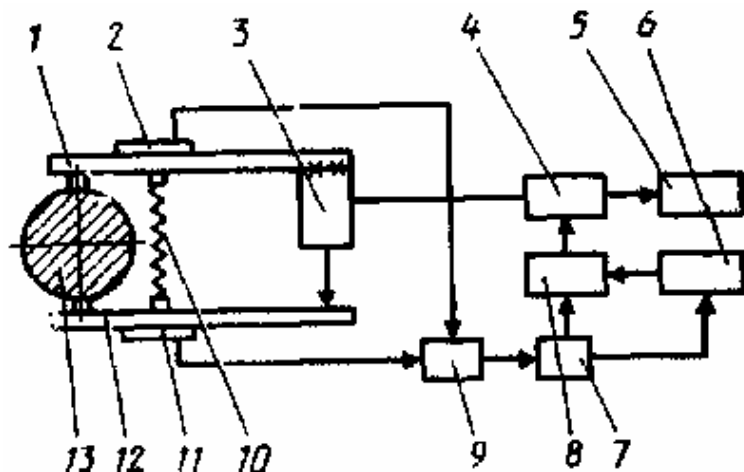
Схема двоточкового пристрою керування та контролю заготовки з основним та додатковим вимірювальними колами
